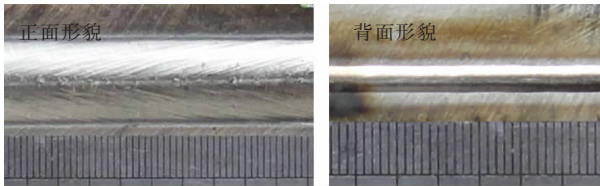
10 mm 厚低碳钢板 DP-TIG 焊接形貌
